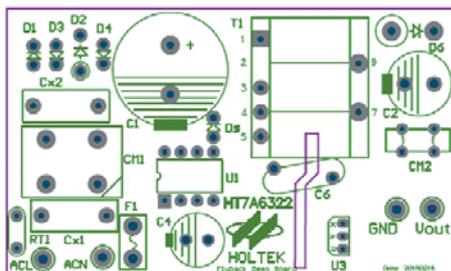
Расположение деталей на плате драйвера (вид сверху)
